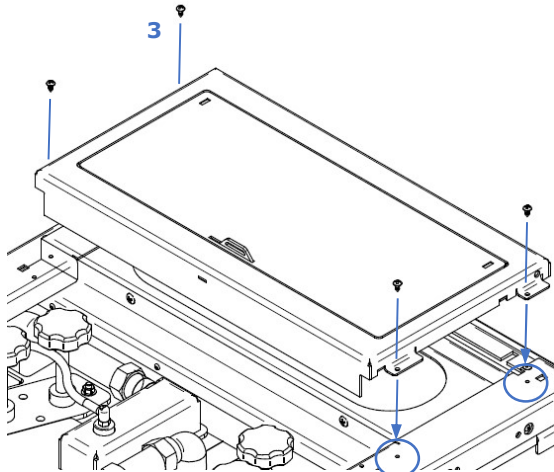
Montaje de la tapa superior Hidro 17 kW y 23 kW
